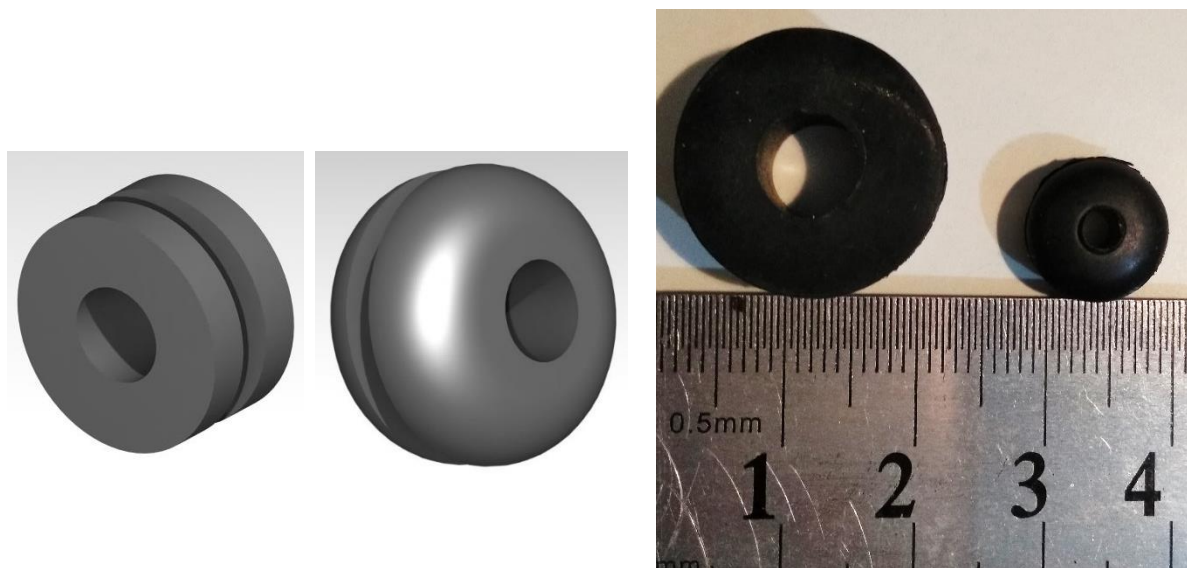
Pasa cables modelados. (Izquierda y centro): en herramienta principal. (Derecha): pasa cables reales.
